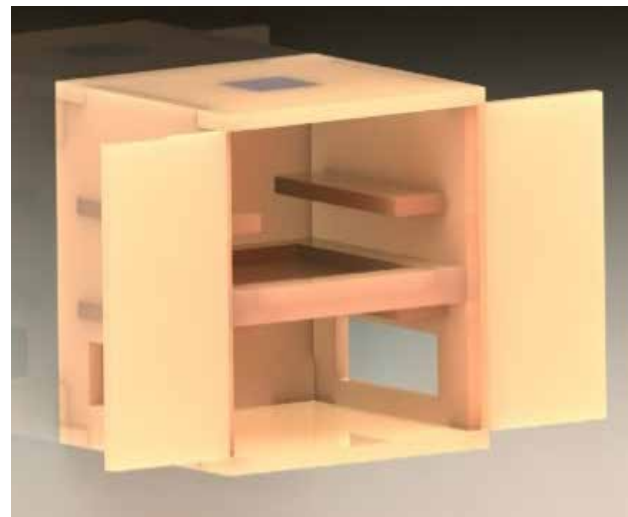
Prototipo deshidratador diseñado con la herramienta CAD – SolidWorks. Fuente: elaboración de las autoras.
